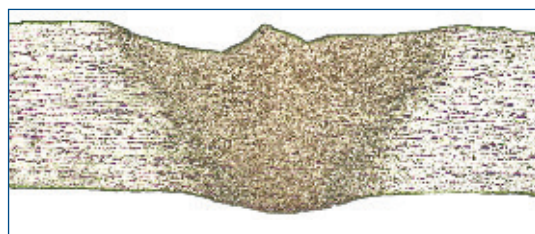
Макроструктура поперечного сечения стыкового сварного соединения сплава АМг6 ($\delta = 1,4$ мм), выполненного плазменным способом со скоростью сварки 30 м/ч, $\times 25$
